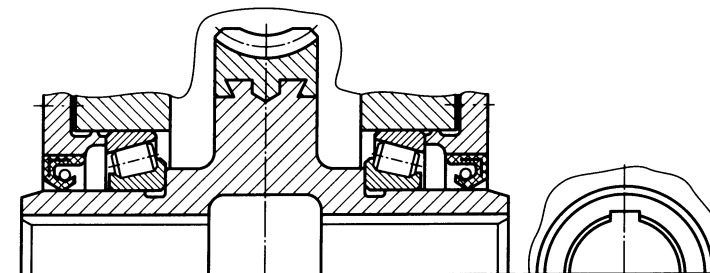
Выходной полый вал навесного червячного редуктора
